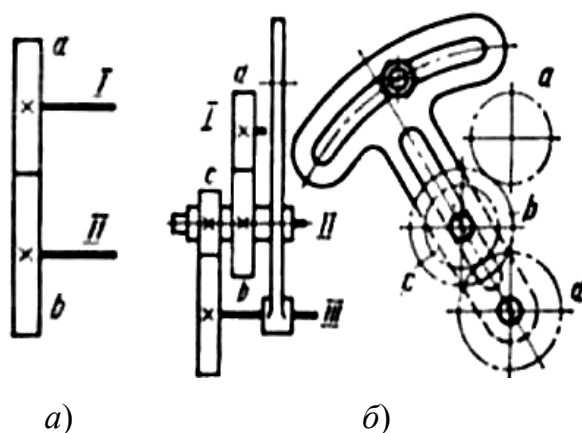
Множительные механизмы со сменными зубчатыми колесами:
